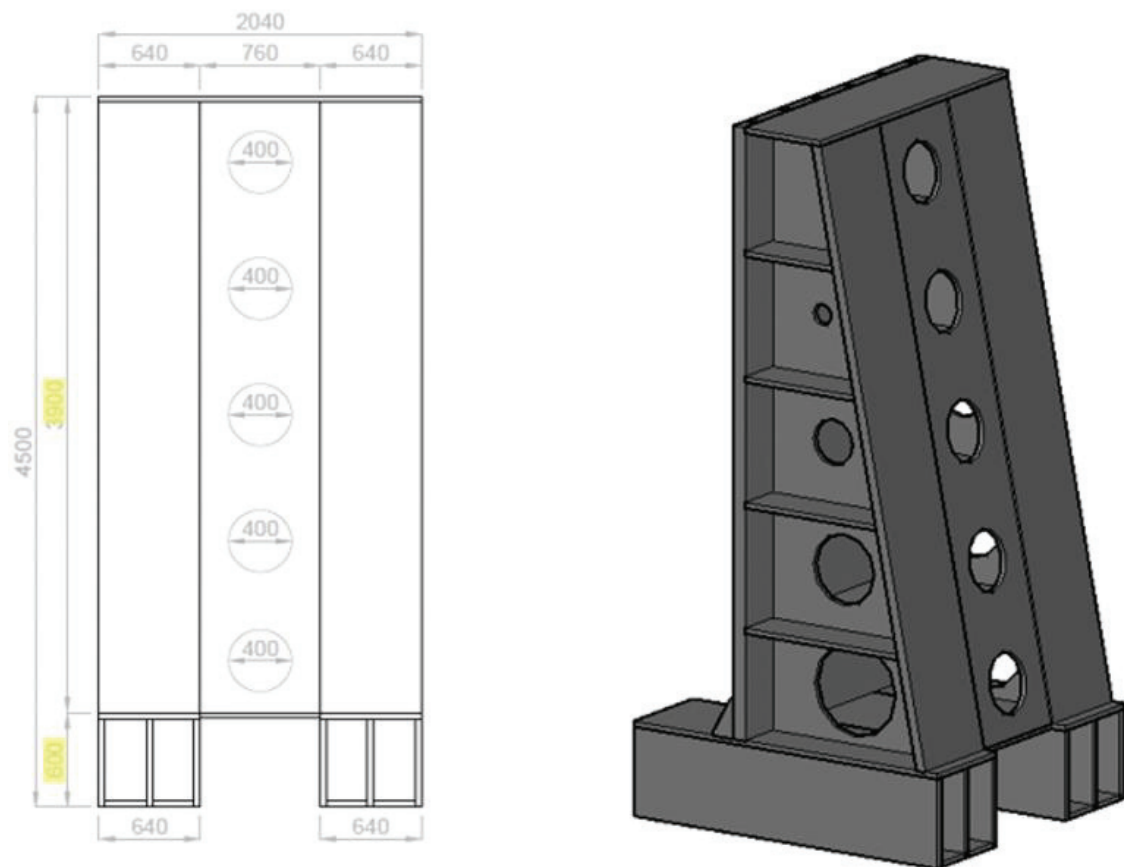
Prospetto posteriore e vista tridimensionale modello struttura N°5
